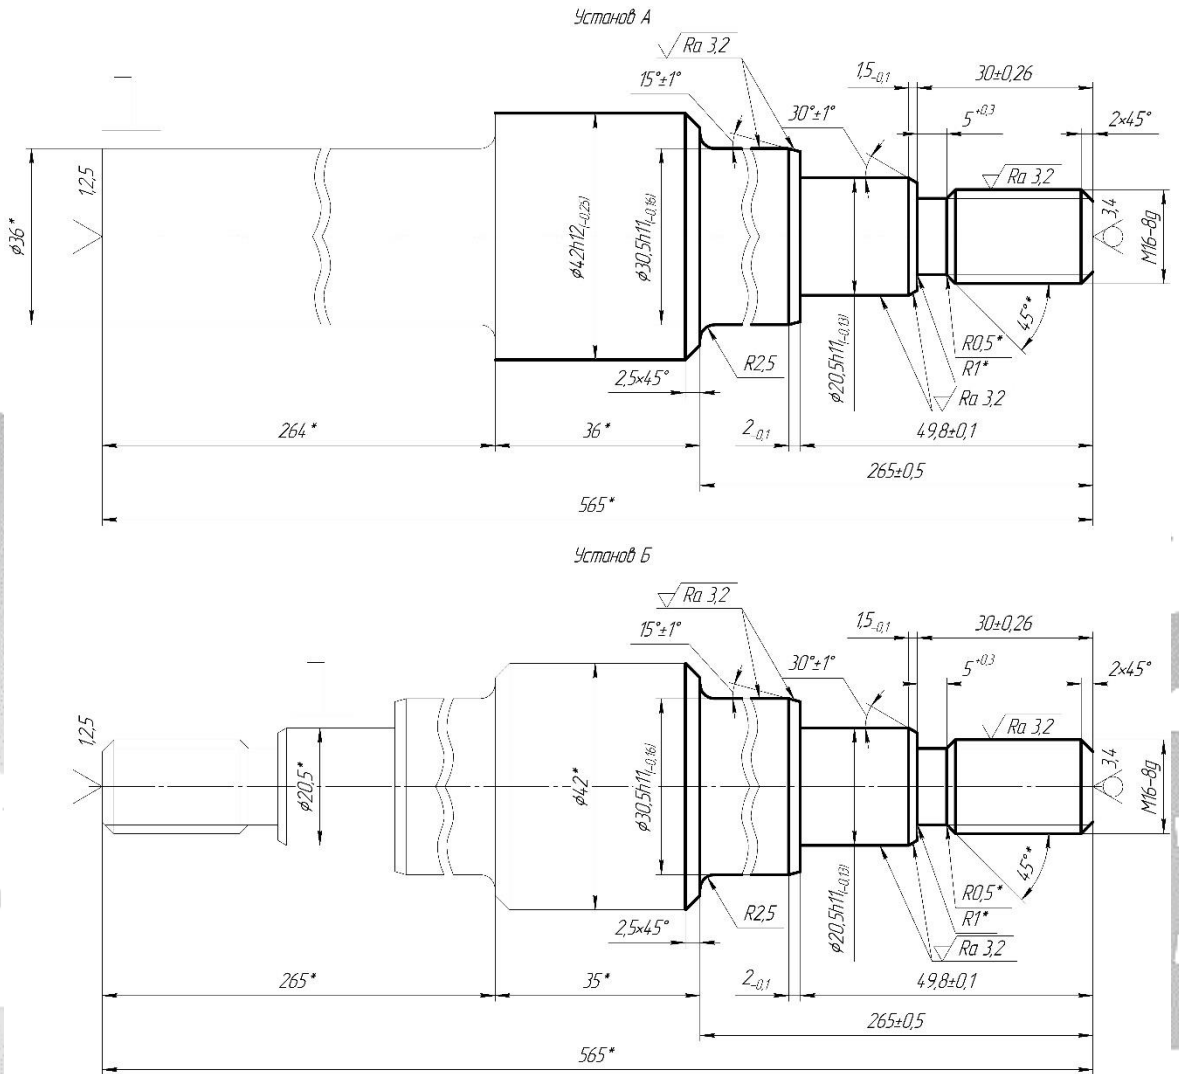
Схема базування заготовки на токарній з ЧПК операції (другий варіант)
